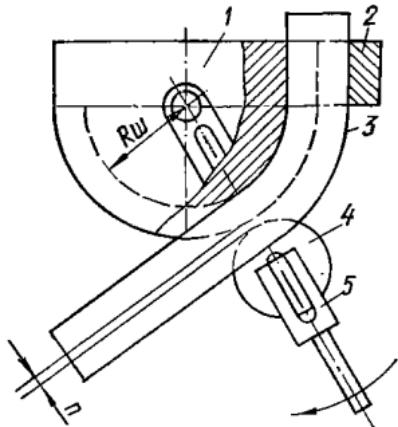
Схема гнутья труб способом обкатки без наполнителя:
